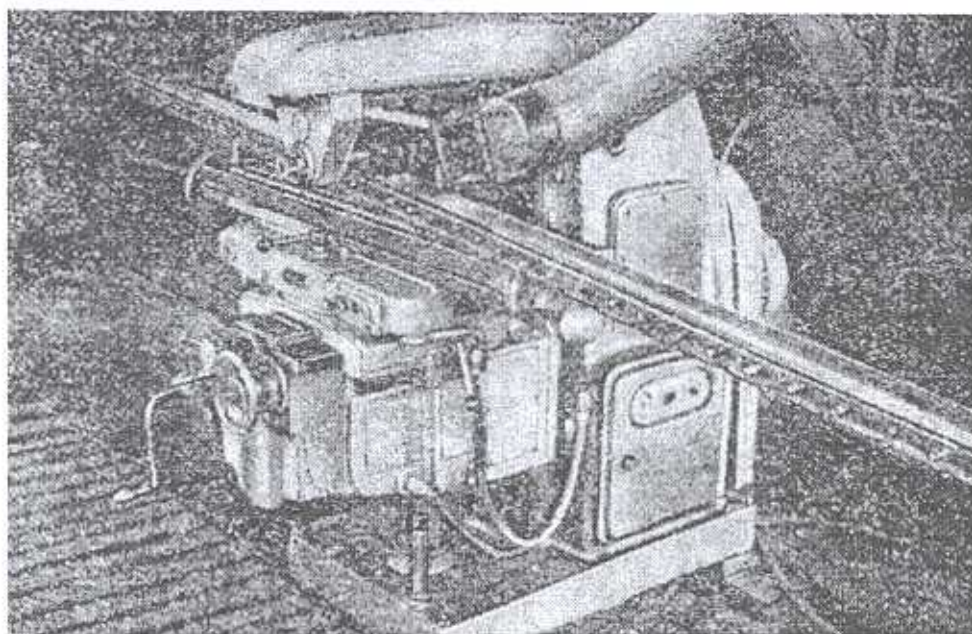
Станок с приспособлением для фрезеровки роторной меди
